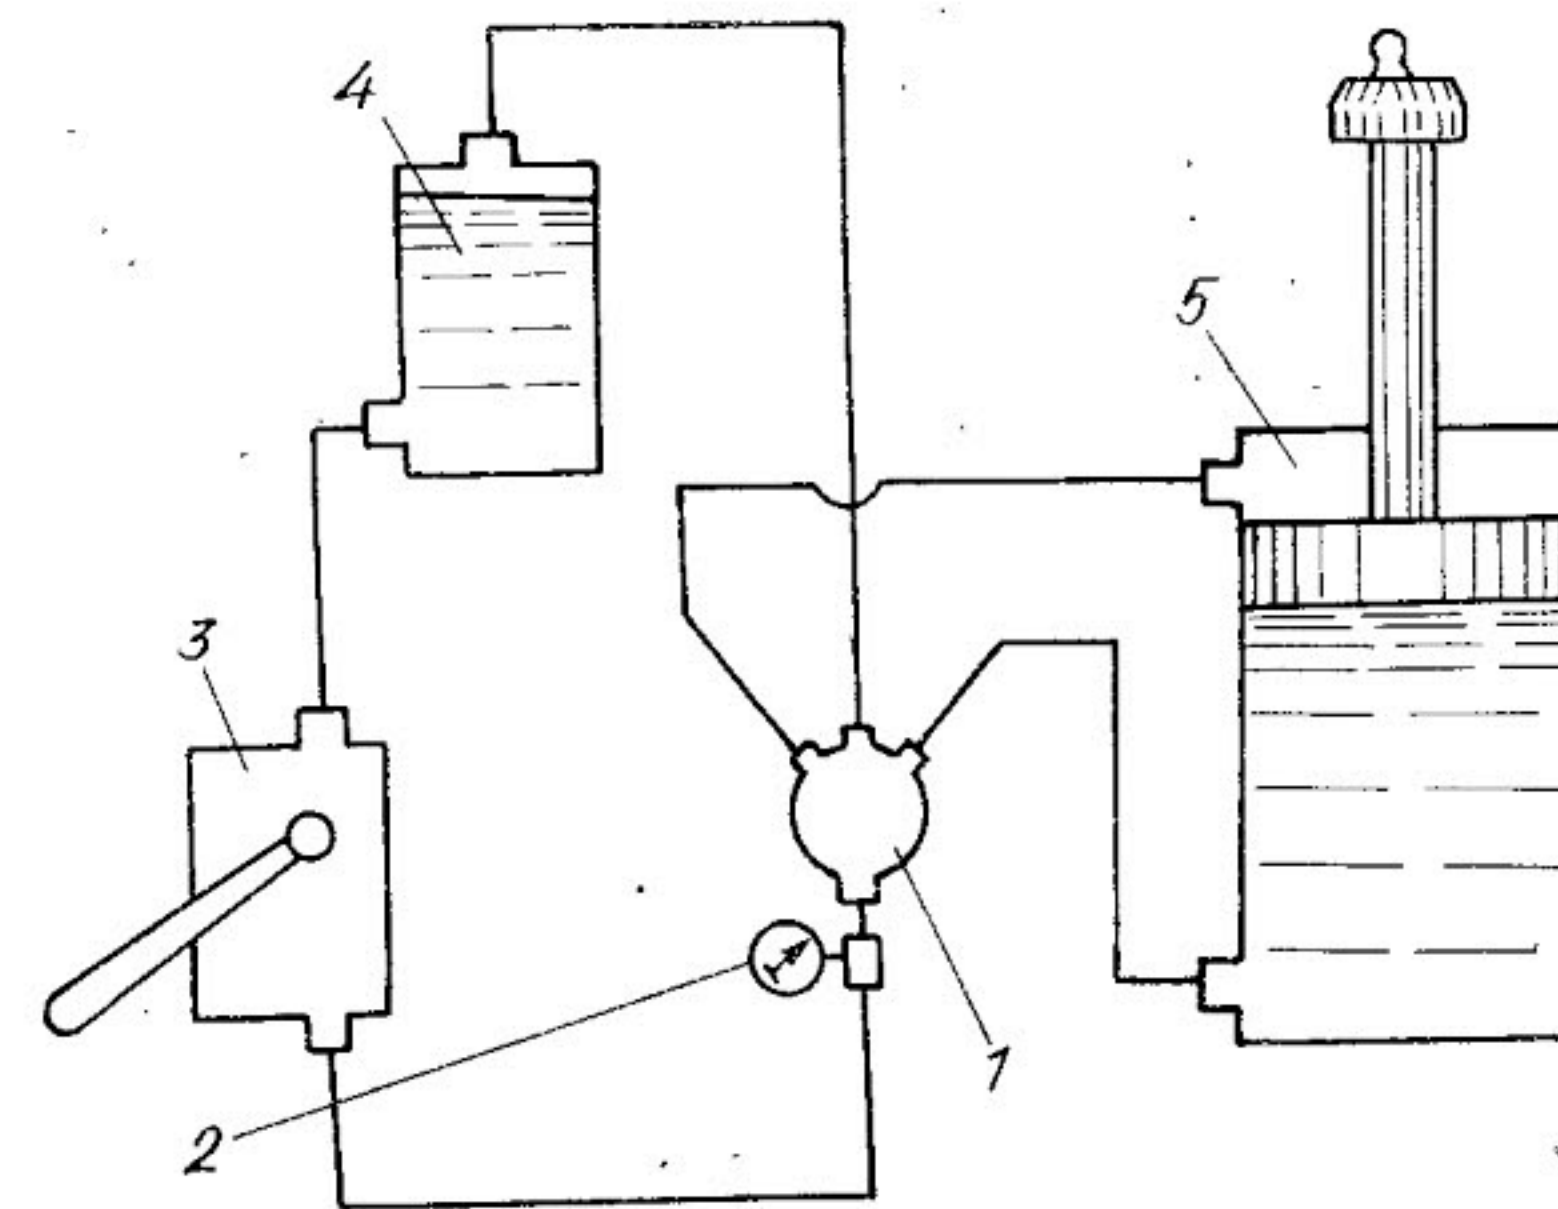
Гидравлическая схема приспособления для испытания наружной подвески:
